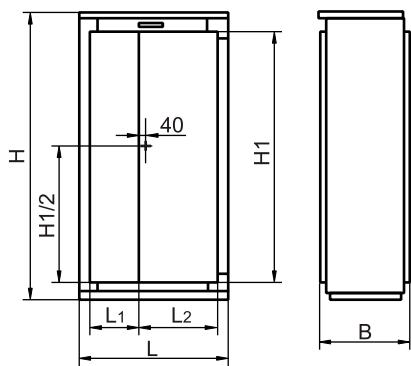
Шкафы ШД5, ШД0 с двусторончатой дверью
